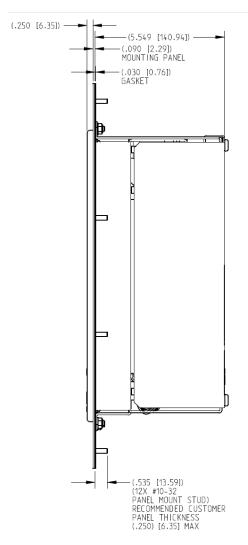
Mounting Outline Diagram for Panel-Mount Models (Габаритная установочная схема моделей для монтажа в вырез панели)
